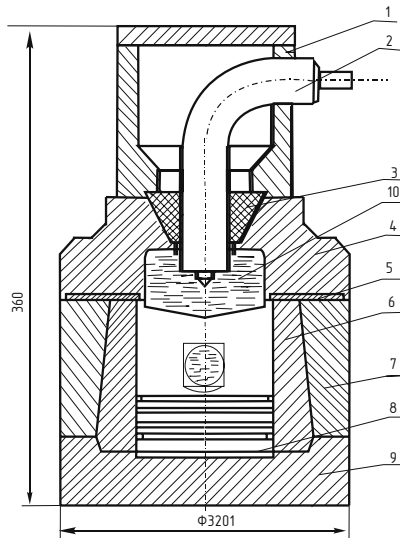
Приспособление для осадки головки: 1 – стакан; 2 – электрод; 3 – гайка; 4 – крышка; 5 – прокладка; 6 – обойма; 7 – контейнер; 8 – прокладка; 9 – плита основания; 10 – камера.
